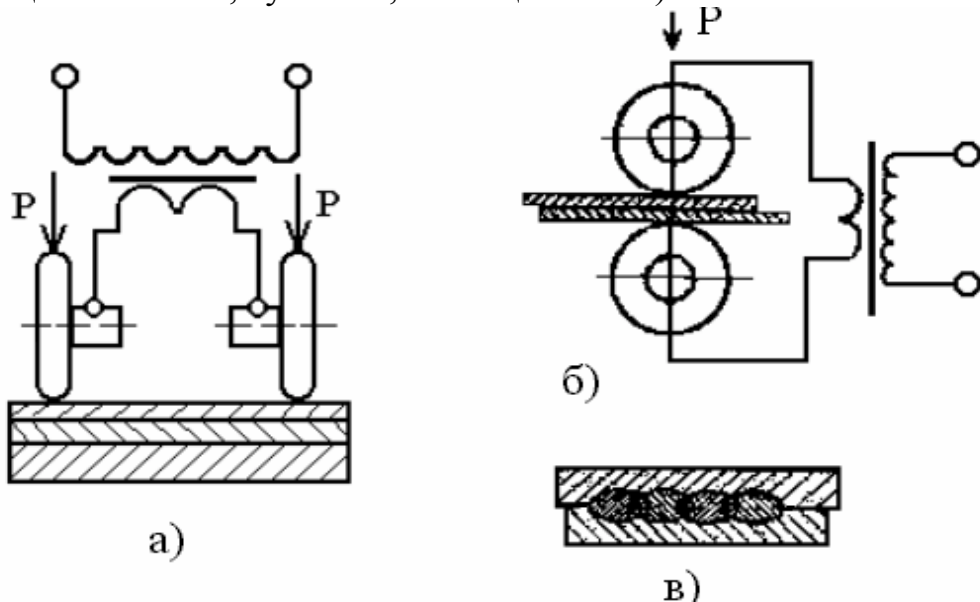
Схемы роликовой контактной сварки: а – односторонняя; б – двухсторонняя; в – разрез сварного шва
